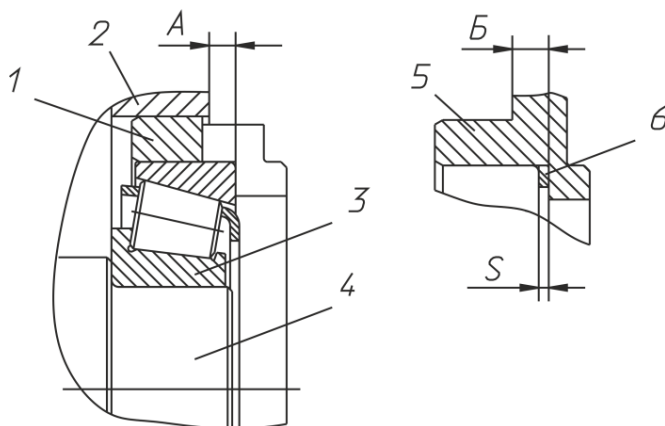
Регулировка осевого зазора в подшипниках промежуточного вала:
